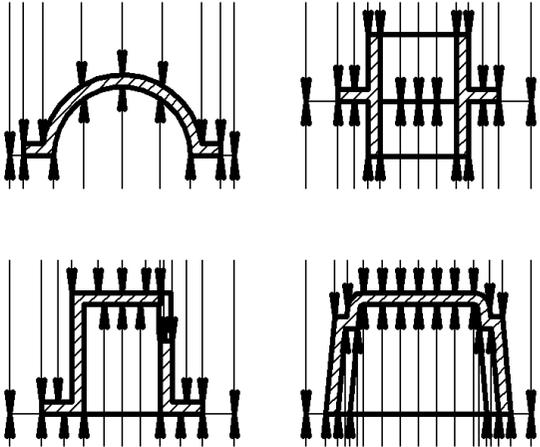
а) деталь, требующая для изготовления пресс-формы с двумя плоскостями разъема; б) – г) детали, требующие для изготовления пресс-формы с одной плоскостью разъема; 1 – изготавливаемые детали; 2, 3, 4 – части пресс-формы
